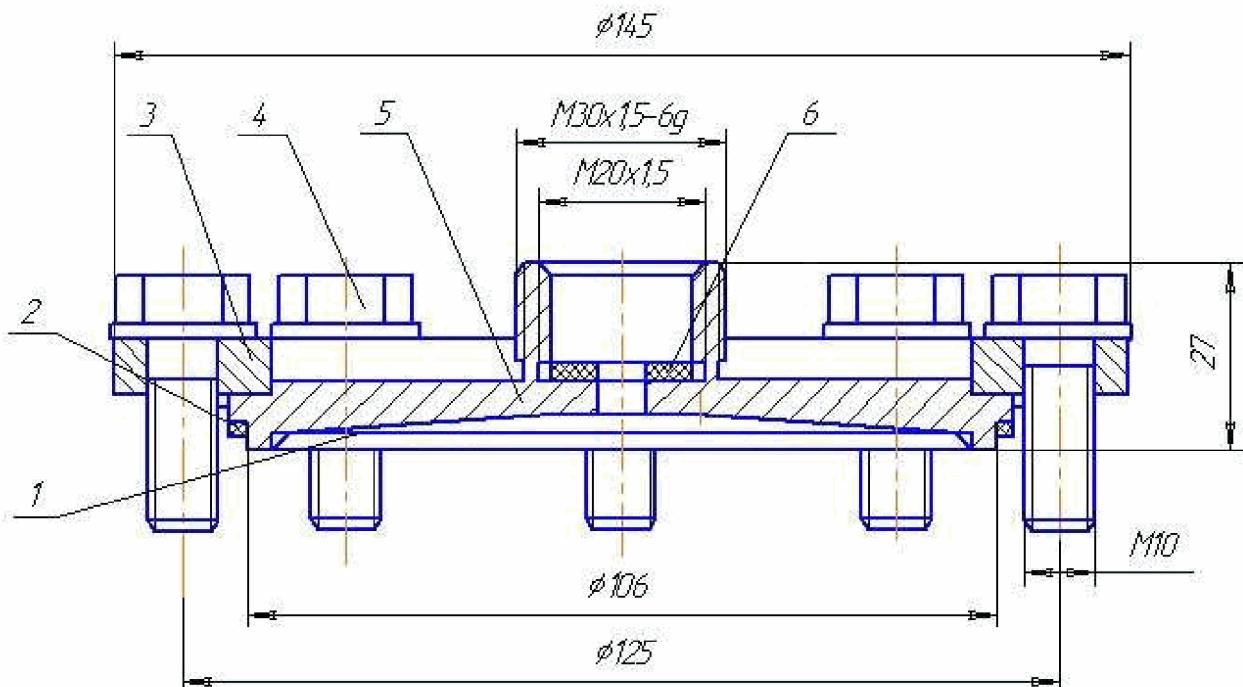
Конструкция, габаритные и присоединительные размеры
